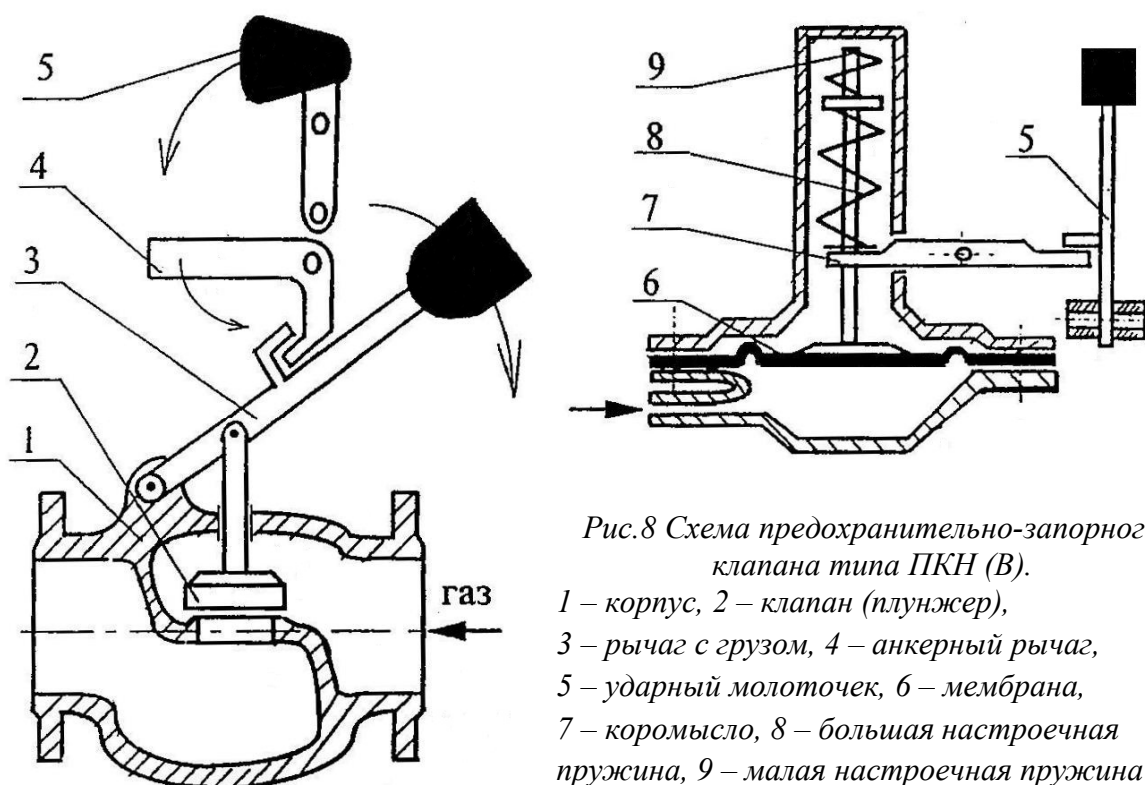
Схема предохранительно-запорного клапана типа ПКН (В).
